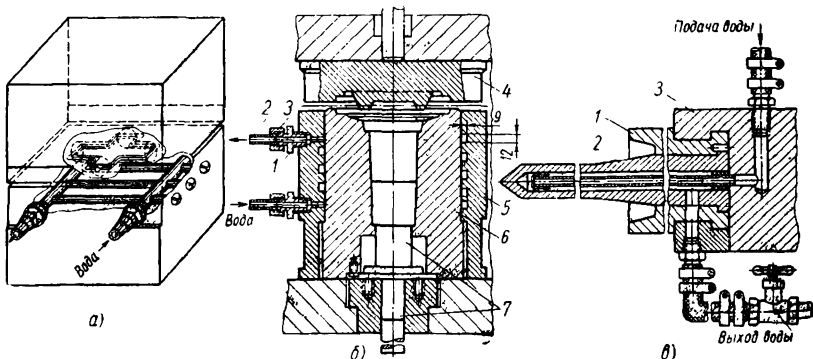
Штампы с внутренним водяным охлаждением: а — кривошипного пресса; б — фрикционного пресса; 1 — штуцер; 2 — ниппель; 3 — гайка; 4 — верхняя вставка; 5 — блок; 6 — нижняя вставка; 7 — толкатель; в — пуансона ГKM; 1 — пуансон; 2 — вставка; 3 — блок пуансонов
